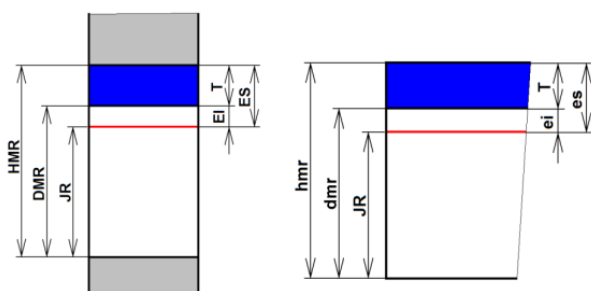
Údaje tolerancí a lícování na strojírenském výkrese
